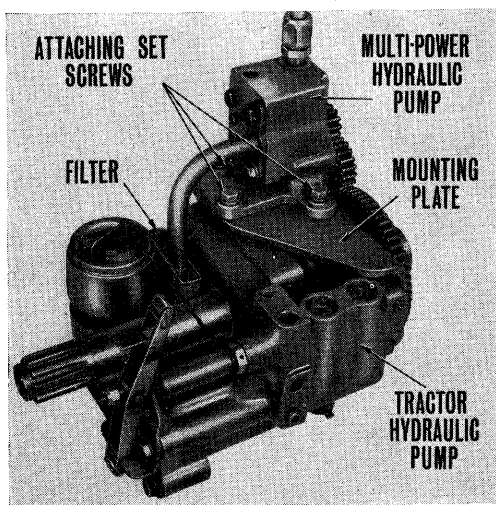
Multipower hydraulik-pumpen monteret på hydraulik-systemets pumpe.
